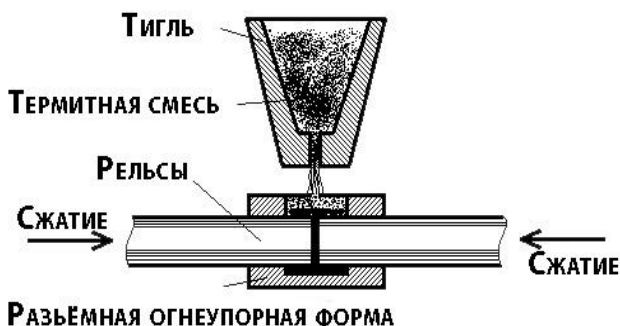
Схема проведения алюминотермитной сварки
